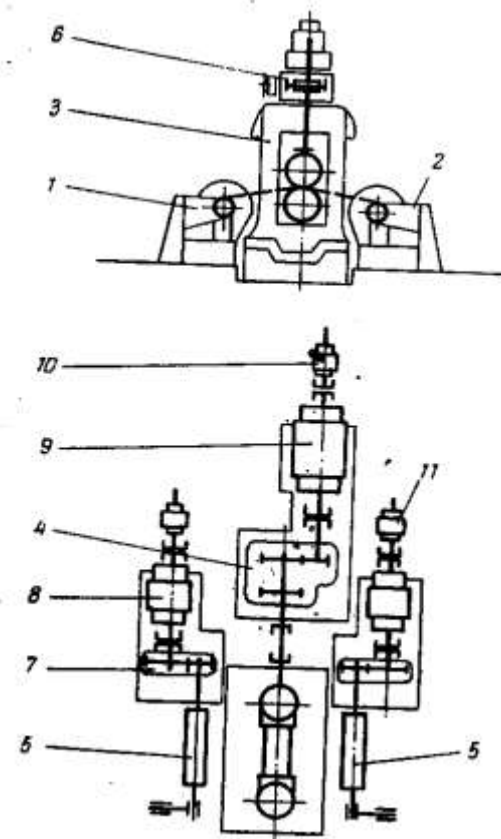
Кинематическая схема фольгопрокатного стана 320x750 с редуктором закрытого типа:
